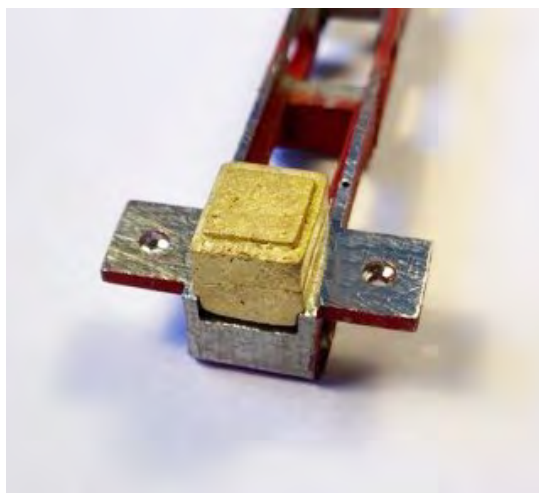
Zylinderverkleidung links im Bild Nietenblech für Steuerungsträger
